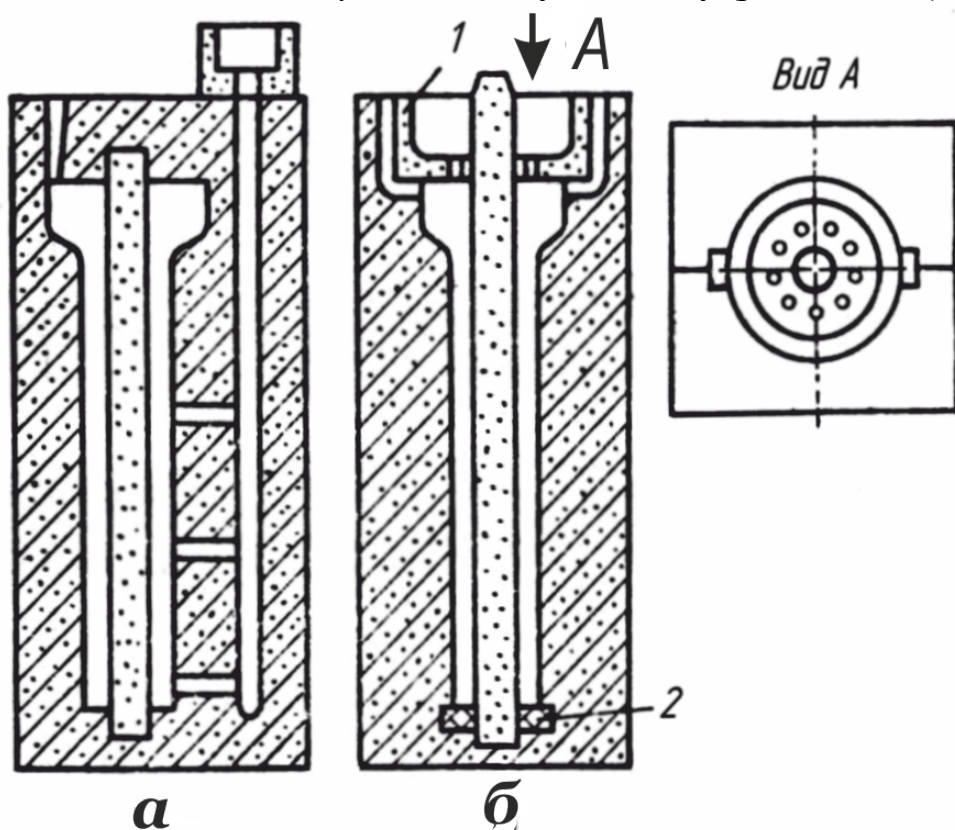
Заливка колонны машины: а – нижний подвод металла; б – дождевая заливка; 1 – литниковая чаша; 2 – шамотный кирпич
